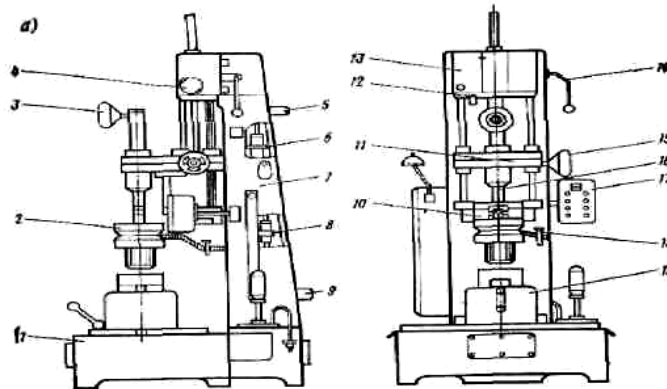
Хонінгувальний станок ЗГ833: а - пристрій: 1 – станина; 2 – шпindelь; 3 – маховик механізму розтиску хону; 4 – кулачки регулювання ходу повзуна; 5 – електродвигун зворотно-поступальної ходи шпинделя; 6 – привід зворотно-поступальної ходи хонінгувальної головки; 7 – колона; 8 – привід обертання шпинделя; 9 – електродвигун приводу обертання шпинделя; 10 – редуктор; 11 – повзун; 12 – штовхач кінцевого вимикача; 13 – коробка подач; 14 – рукоятка реверсу; 15 – маховик ручного введення хону; 16 – повідець хонінгувальної головки; 17 – пульт управління; 18 – кран охолодження; 19 – пристосування для обробки гільз або блоків.
